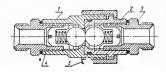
Запорное устройство маслопроводов: 1— клапан маслопровода; 2— клапан шланга; 3— шланг; 4— маслопровод; 5— накидная гайка.
